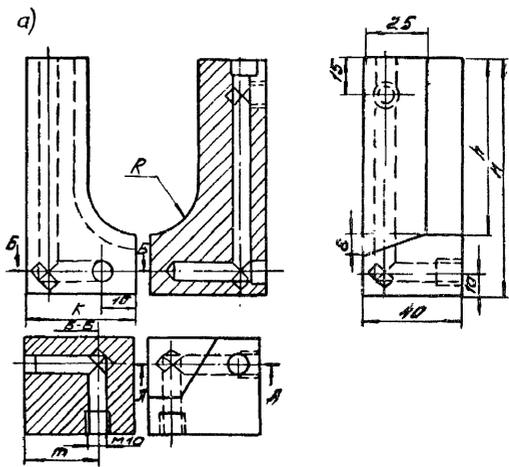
Рабочие чертежи медных форм для сварки втавр спаренных стержней.
